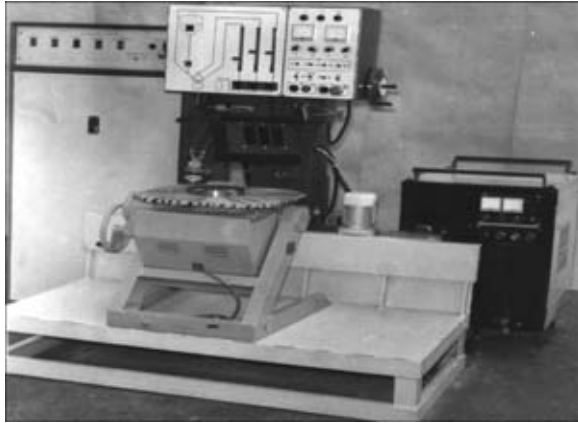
Универсальная установка ОБ2184 для плазменно-порошковой наплавки
